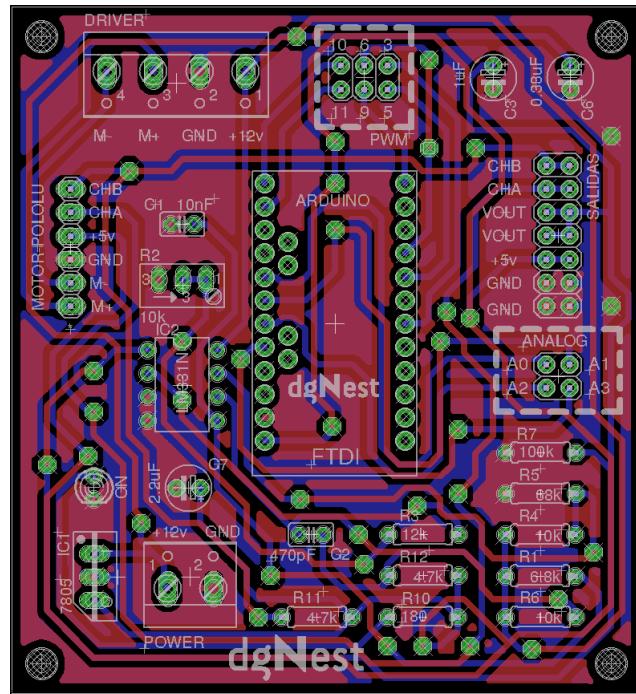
PCB (board) conversor f/v generado en eagle
